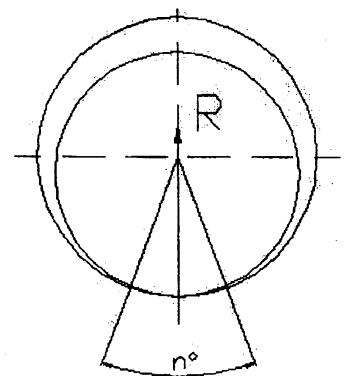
Схема контакта опорной поверхности вала - буксовая втулка
